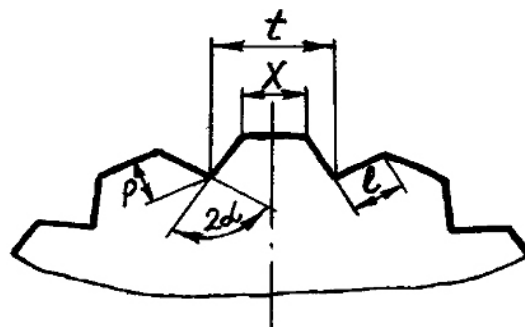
Профиль рифлений на боковой поверхности рабочей части пробивного пуансона
